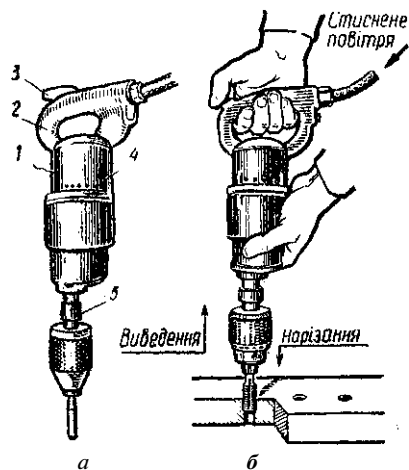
Різьбонарізувач ПНР-8 легкого типу з пневматичним приводом: а — будова; б — прийом роботи
